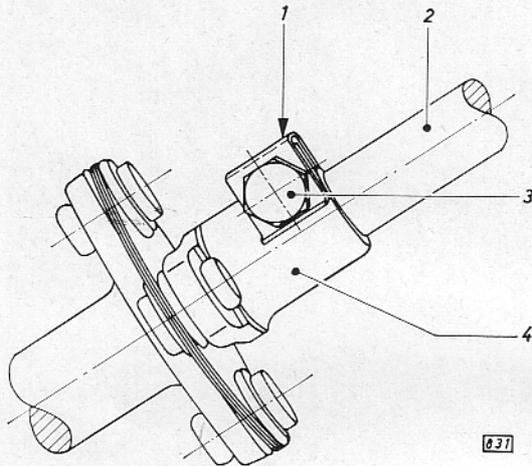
Sicherung der Klemmschraube am Lenkspindel flansch
